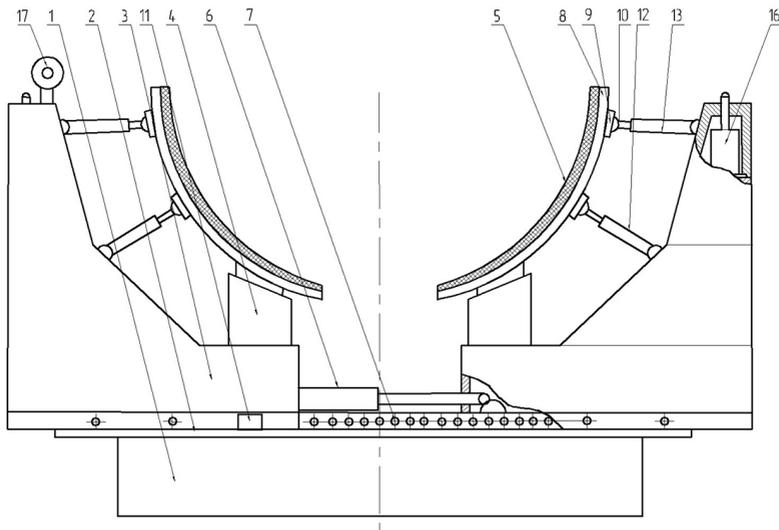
Кониковое зажимное устройство: 1 – рама; 2 – направляющая; 3 – подвижный корпус; 4 – жесткая стойка; 5 – фрикционная накладка; 6 – гидроцилиндр; 7 – фиксирующее отверстие; 8 – металлический гибкий лист; 9 – ребро жесткости; 10 – шарнирное соединение; 11 – фиксатор; 12, 13, 16 – гидроцилиндры; 14 – страховочный трос; 15 – крюк; 17 – блок
